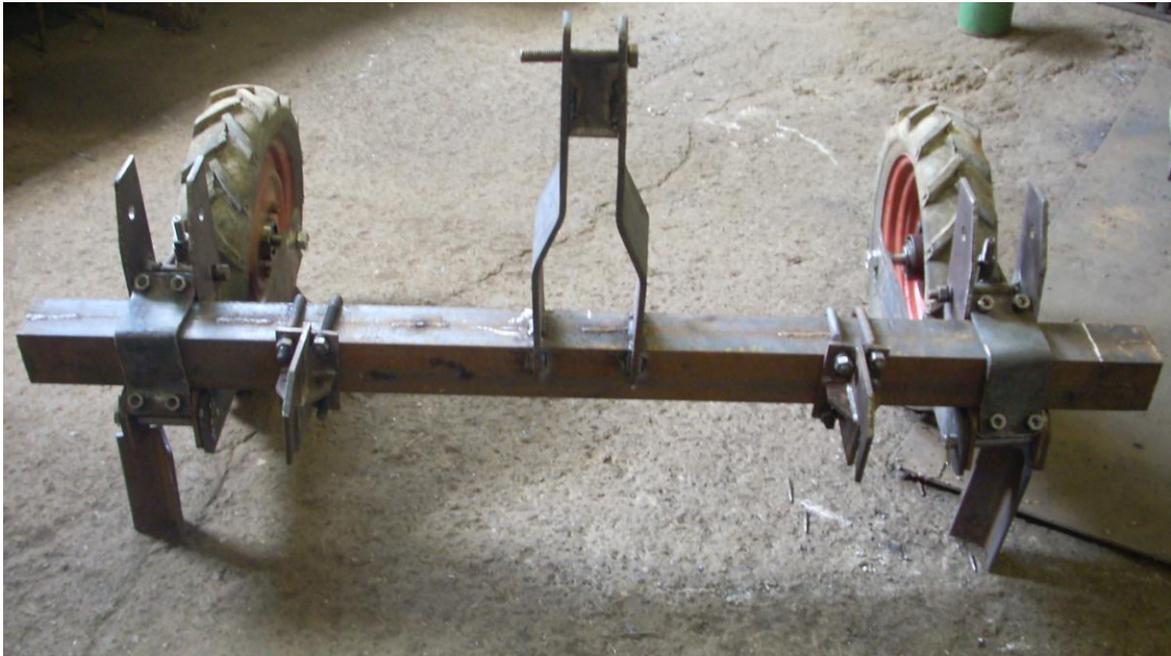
Vue de face, attelage et bloc roue sur châssis.
